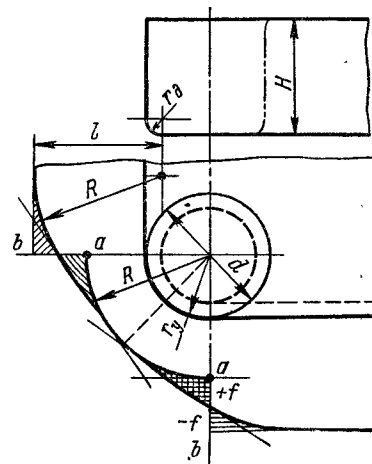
Построение контура заготовки для низких прямоугольных коробок, вытягиваемых в одну операцию
